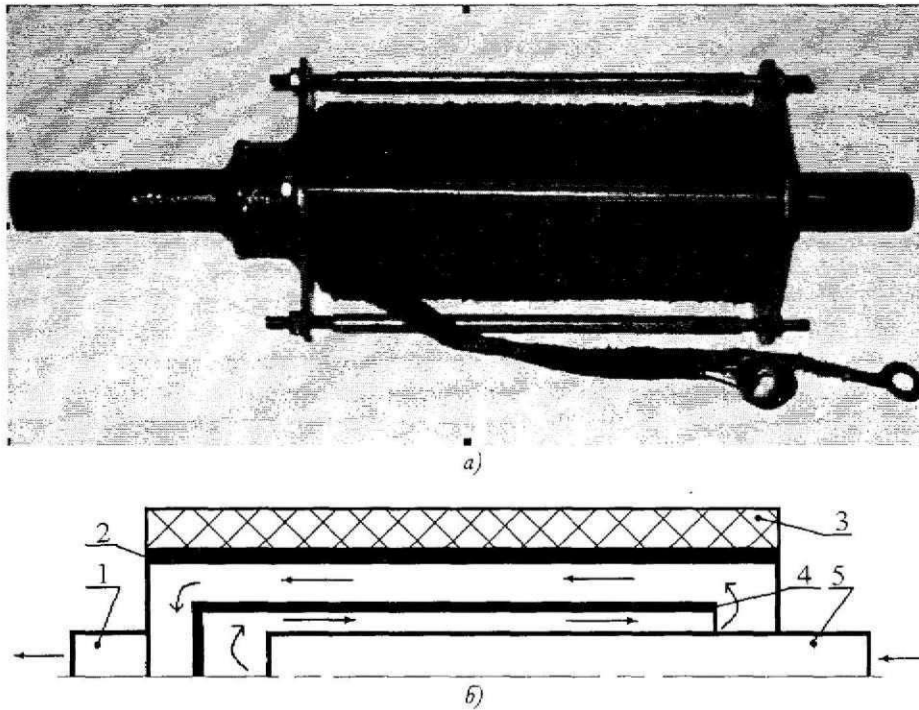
Общий вид а) и конструктивная схема б) электромагнитного аппарата: 1 – отводящий патрубок; 2 – корпус; 3 – обмотка; 4 – вставка; 5 – подводящий патрубок
